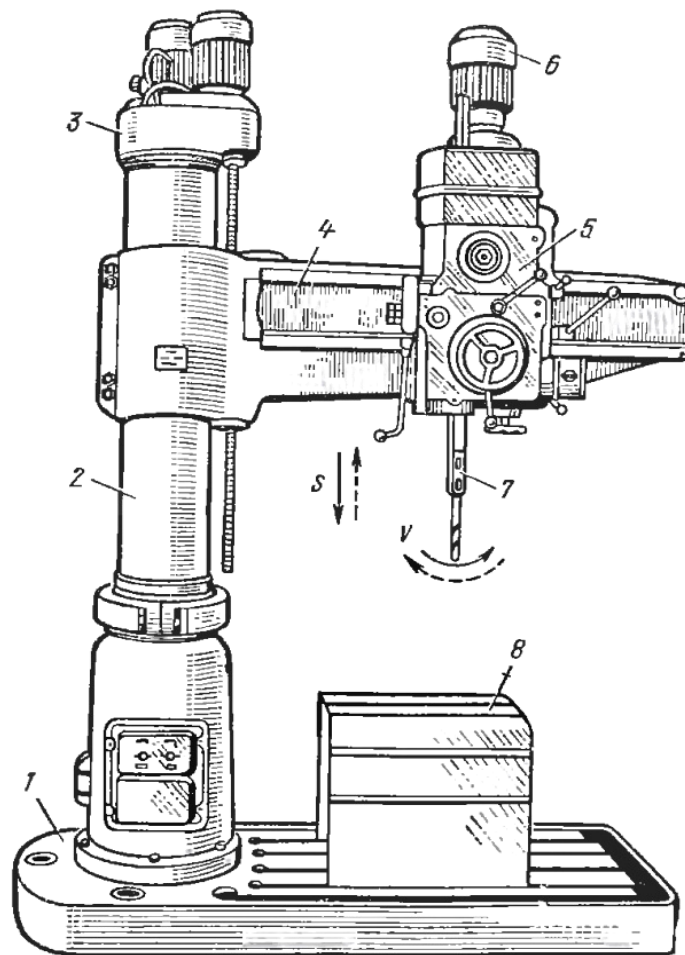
Загальний вид радіально-свердлильного верстата
